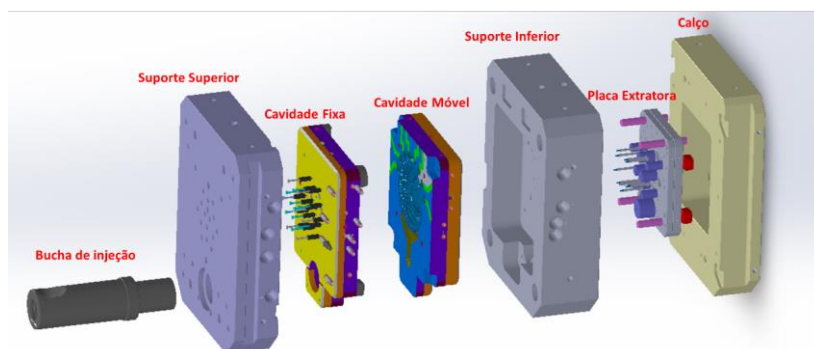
Visão macro dos elementos construtivos de um molde para injeção de alumínio (Autor)
